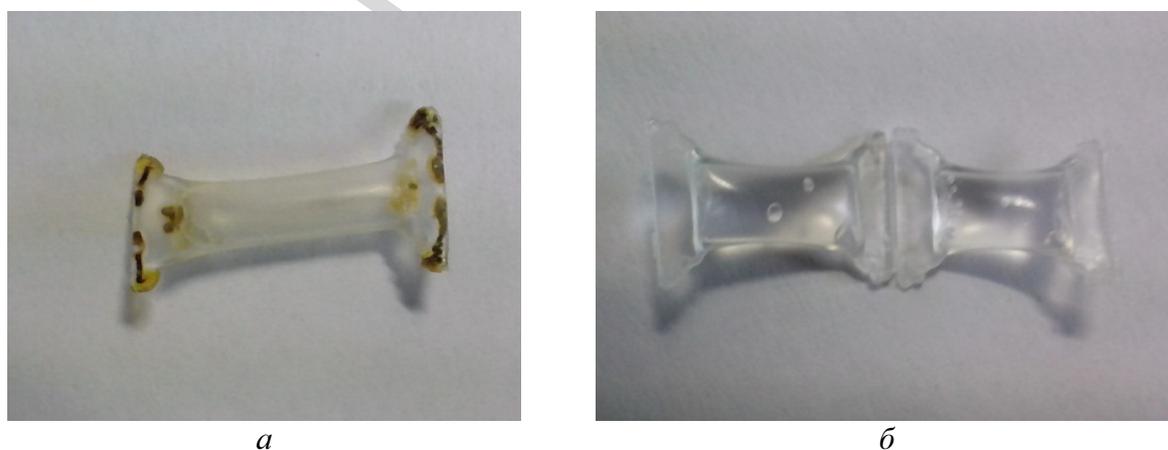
Вид сварных соединений полимерной трубки различных производителей:
